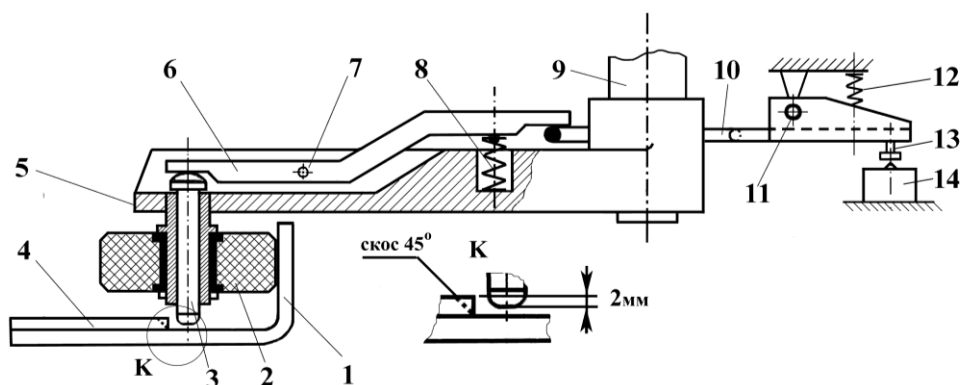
Схема конструкции привода контакта реверса движения створок:
